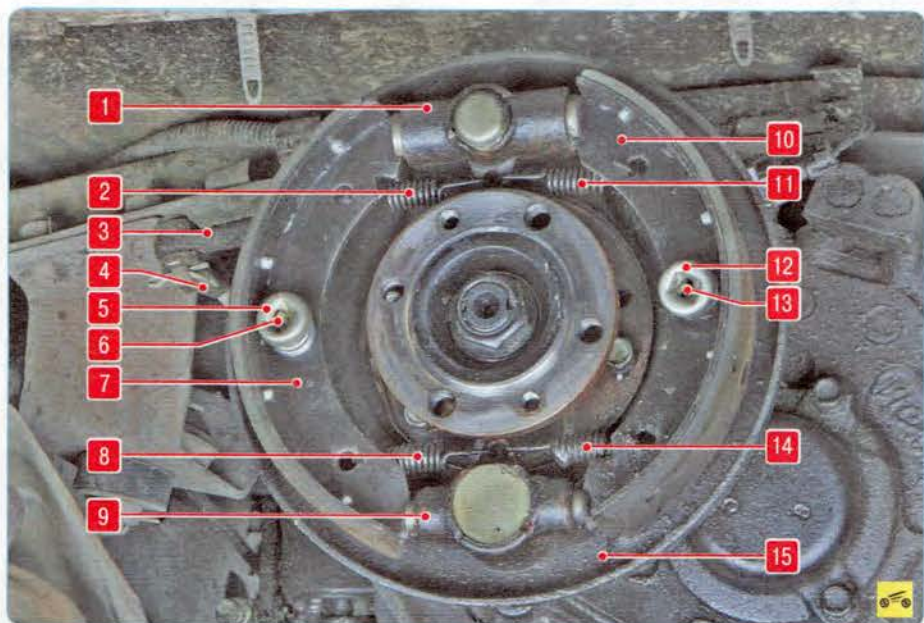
Детали барабанного механизма стояночного тормоза: 1 – разжимное устройство; 2, 8, 11, 14 – стяжные пружины; 3 – рычаг; 4 – вилка троса привода стояночного тормоза; 5, 12 – чашки пружин опорных стоек; 6, 13 – опорные стойки колодок; 7, 10 – колодки; 9 – регулировочное устройство; 15 – тормозной щит
